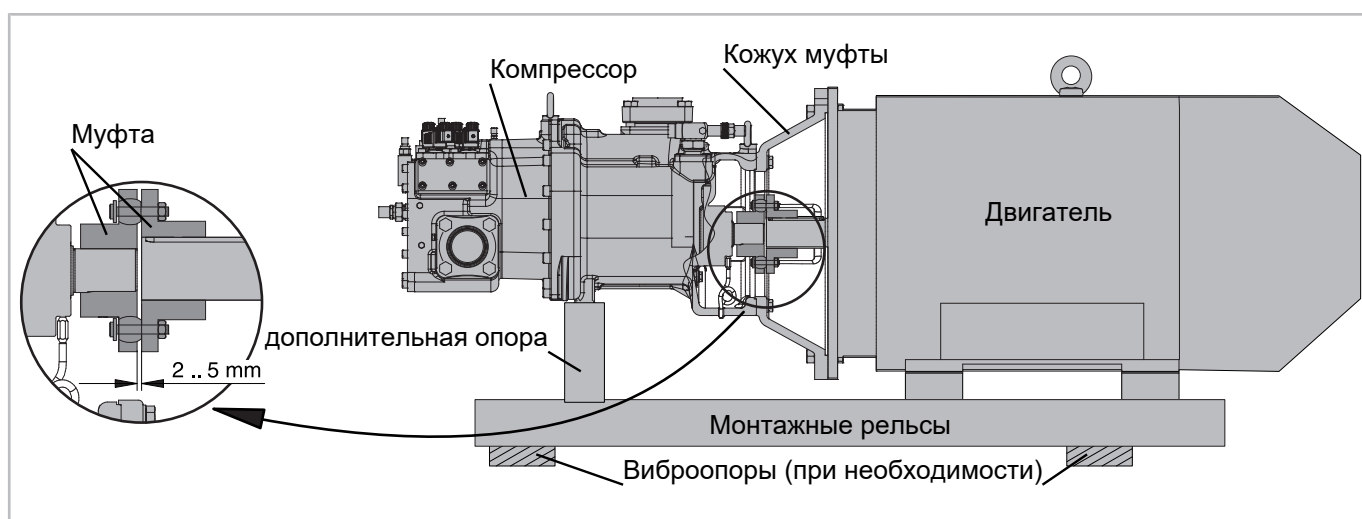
Пример для компрессора OS.85 с двигателем и муфтой
